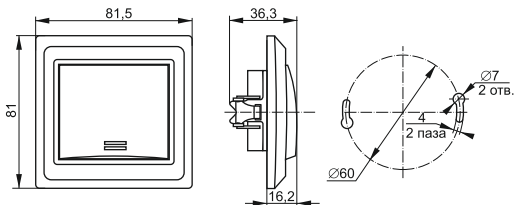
Габаритные размеры выключателя BS10-1-1-BB
